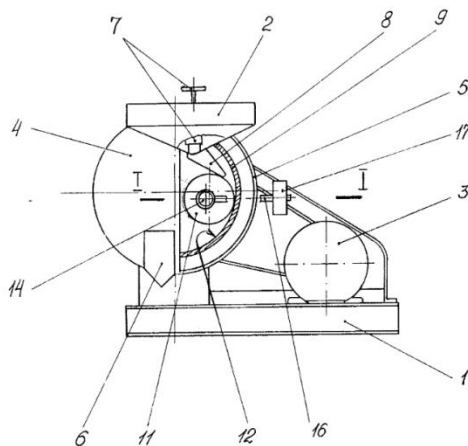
Схема плющильного станка. 1 – рама; 2 – бункер для подачи зерна; 3 – привод; 4 - вальцовое плющильное устройство; 5 – кожух; 6 - лоток для выдачи плющеного зерна; 7 – регулировочный затвор; 8 - зернораспределительная течка для подачи зерна; 9 – обечайка внутреннего плющения; 10 – диск; 11- валец; 12 – внутренняя поверхность обечайки; 13 – подшипниковая ось; 14 – вал; 15 – опорный подшипник; 16 – рычаг; 17 – груз.
